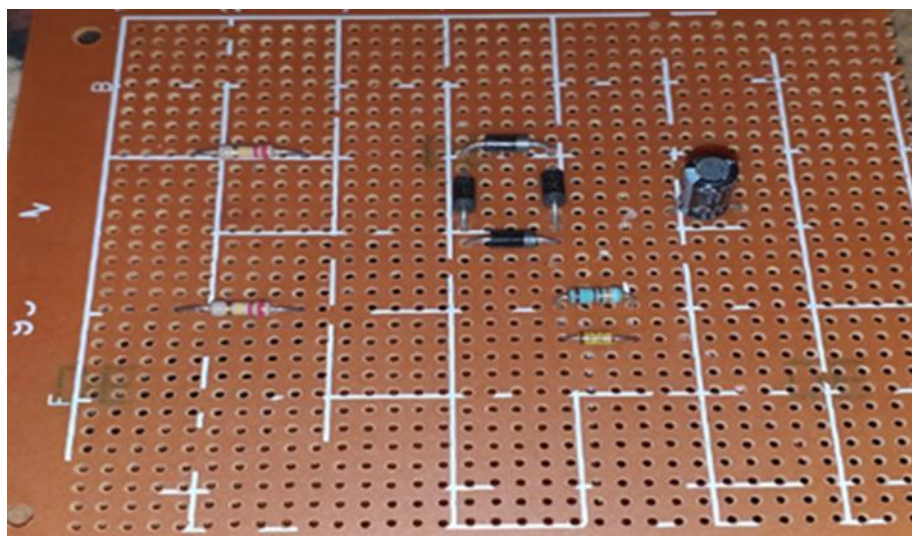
Connectez les composants du capteur à la plaque de soudure.
